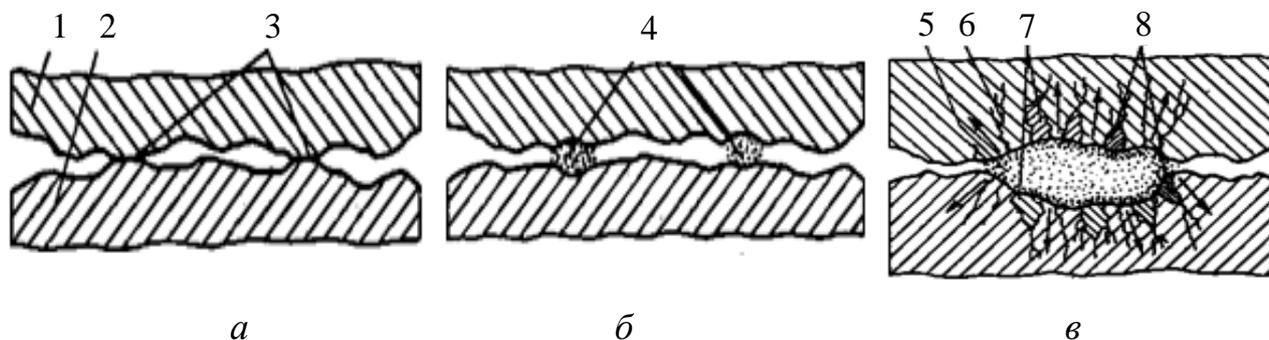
Механизм изнашивания металлических поверхностей при фреттинг-коррозии: 1, 2 – контактирующие детали; 3 – точки контакта поверхностей; 4 – мелкие зарождающиеся каверны; 5 – общая большая каверна; 6 – трещины; 7 – отколовшиеся объемы металла; 8 – отколовшиеся частицы с твердой структурой
